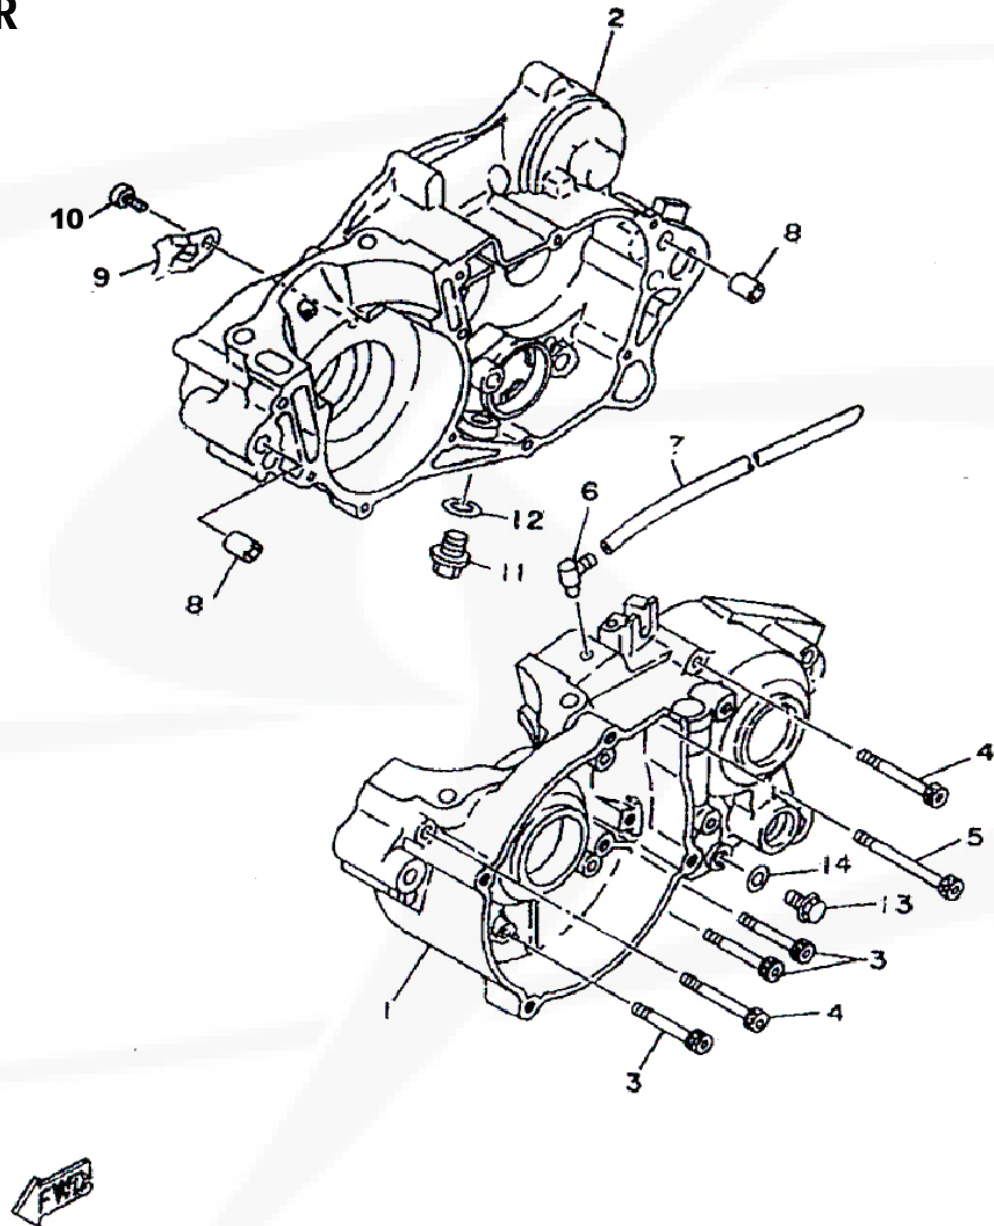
CARTER / CRANKCASE / CÁRTER
